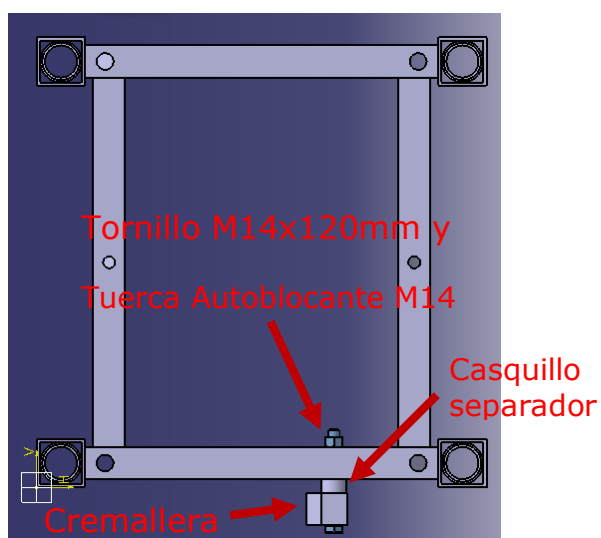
Disposición de la cremallera y fijación de la misma al mástil. Vista en planta
